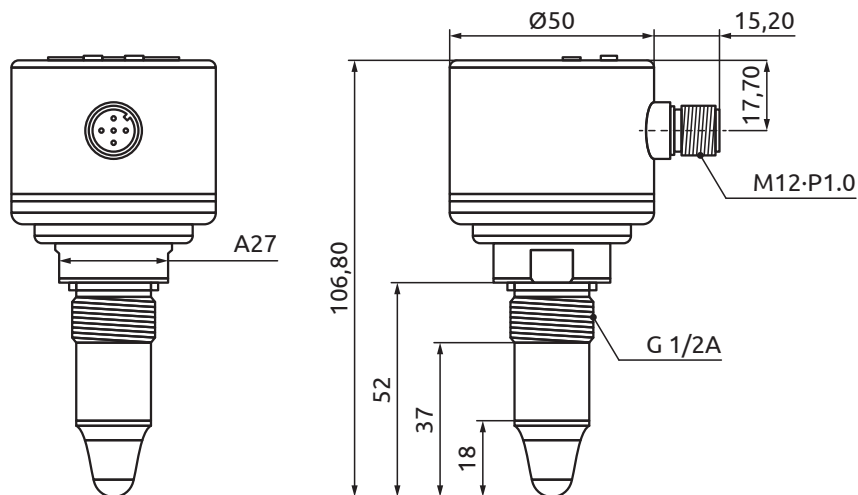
Габаритный чертёж электромагнитных датчиков ELS-052-T
